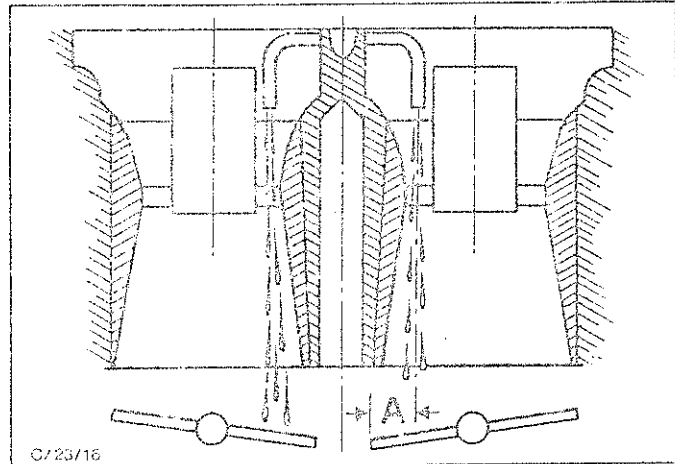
Spritzrichtung der Spritzrohre (Beschleunigerpumpe) einstellen. Maß "A" siehe Technische Daten
